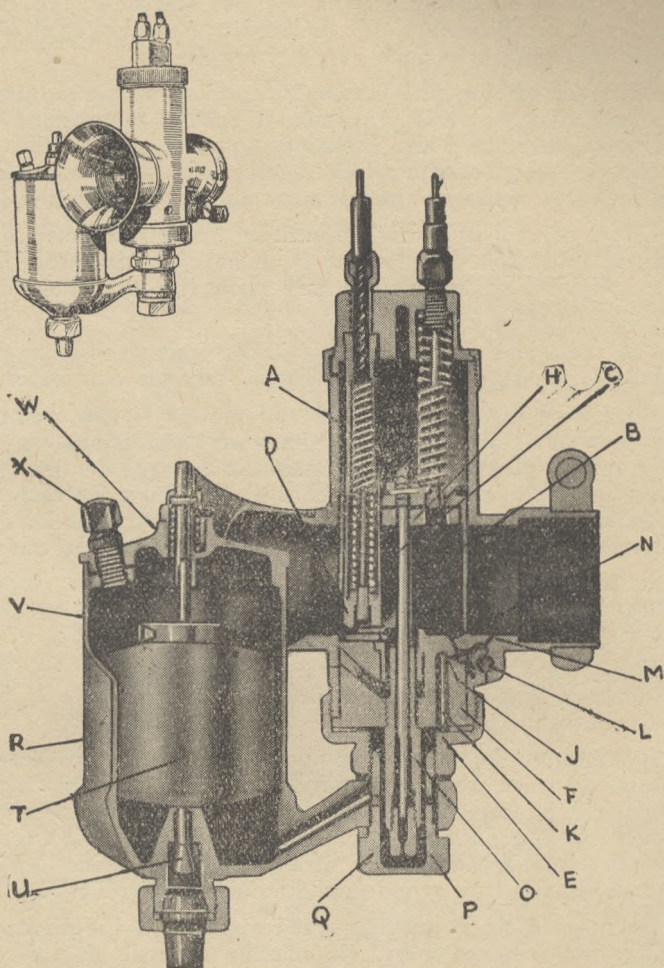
Vue extérieure et coupe du carburateur AMAC.
